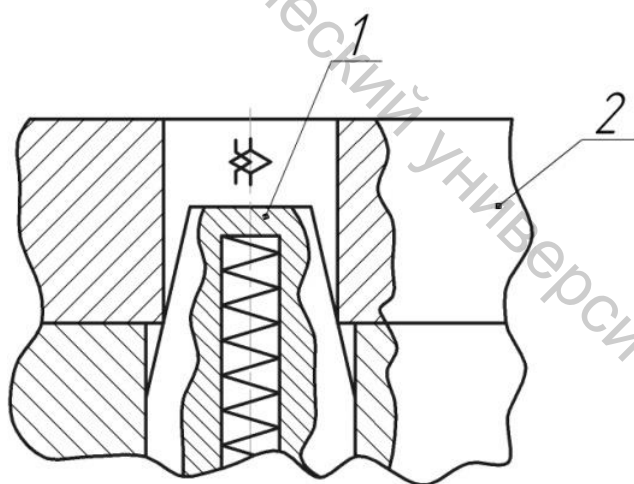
Установка заготовки с помощью конического пальца
